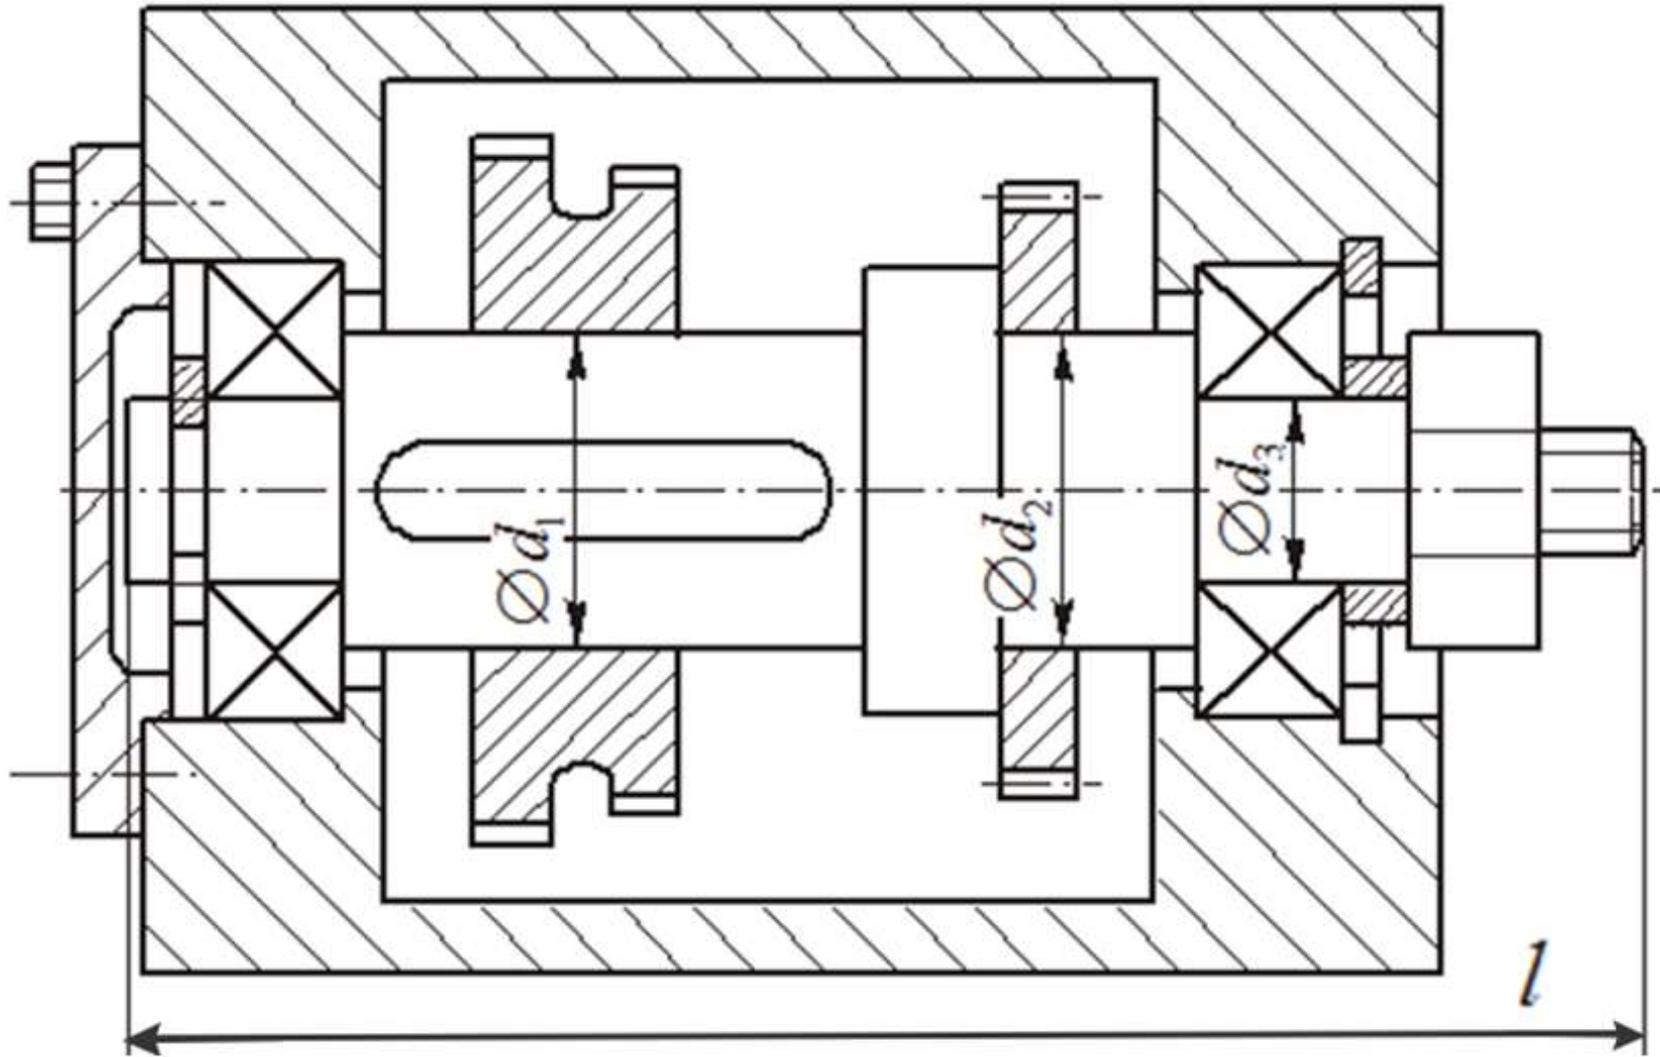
Пример сборочного эскиза редуктора без указания размеров и посадок (задание на ИДЗ-4)
